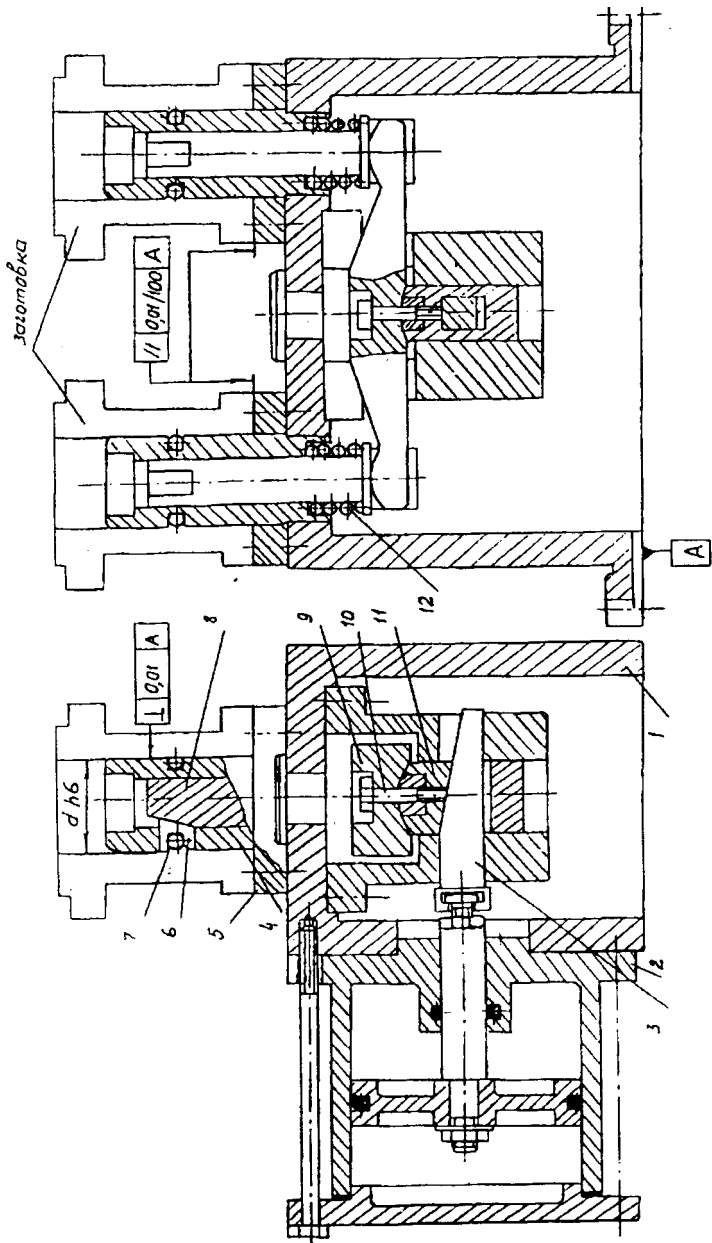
Двухместное фрезерное приспособление с механизированным зажимом
